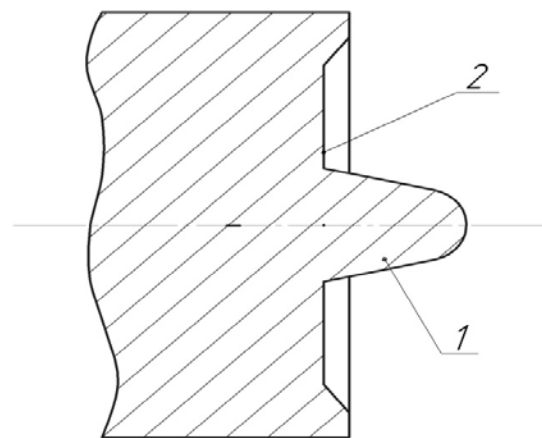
Схематичне зображення робочого інструмента для зварювання тертям із перемішуванням: 1 – штифт; 2 – поверхня плеча
